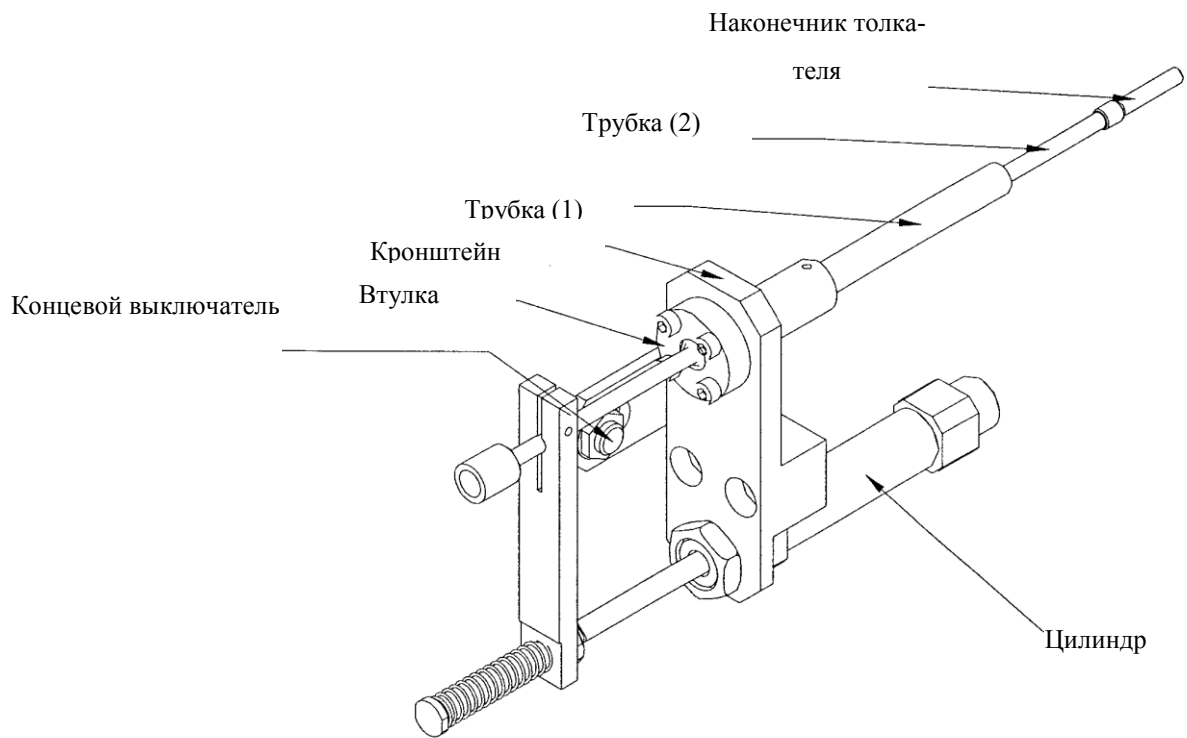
Приспособление для выталкивания деталей вперед/ обнаружения
